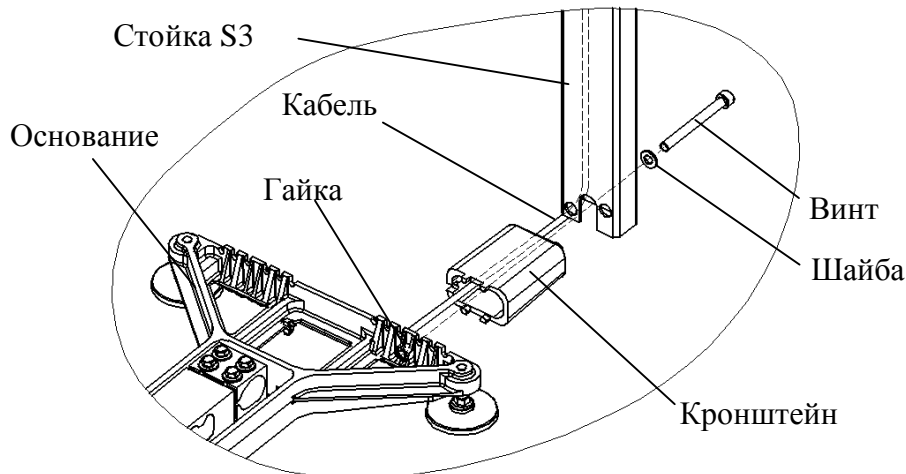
Крепление прямоугольной стойки к основанию весовой платформы ТВ-S\
